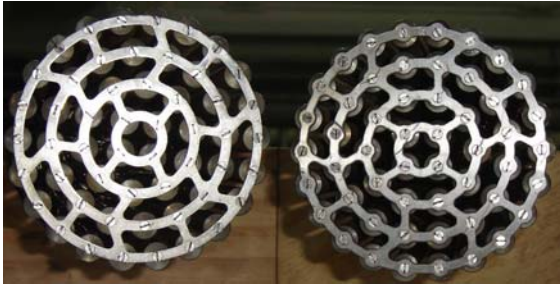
Grillas de diseño similar al EC Embalse y con sección de refuerzo.
